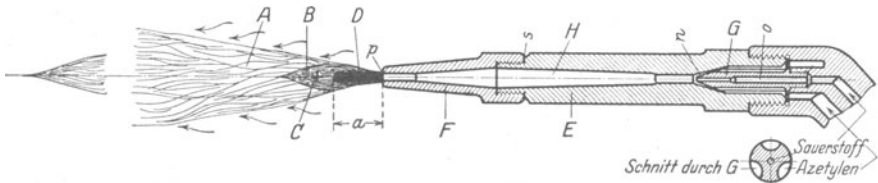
Vorderteil des Azetylenbrenners und Schweißflamme.
